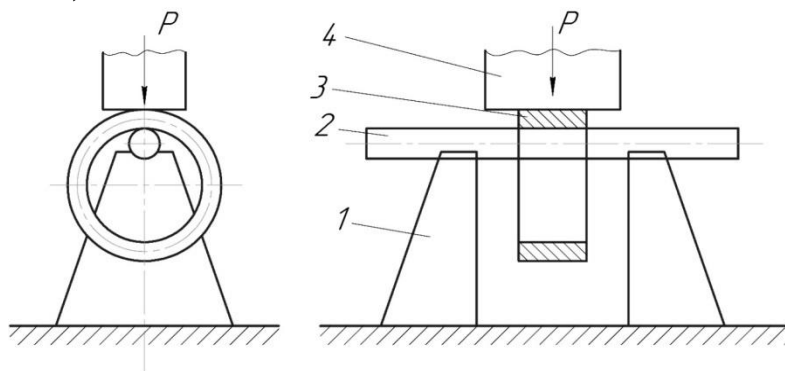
Схема раскатки кольцевых заготовок на ковочной оправке
